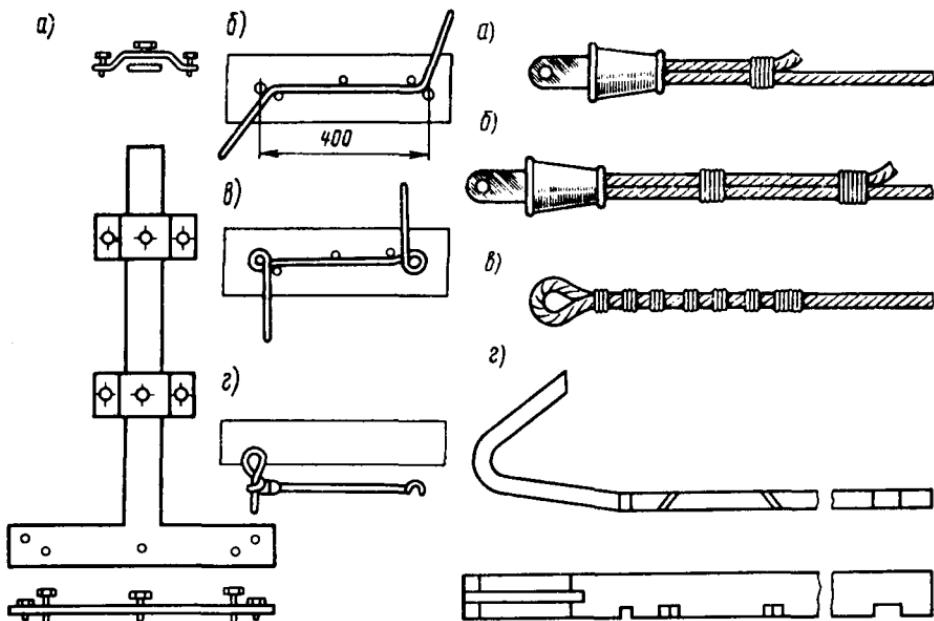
Приспособление для закрутки проволоки: *а* — приспособление; *б* — закладка проволоки; *в* — образование очка вокруг стоек; *г* — закрутка
